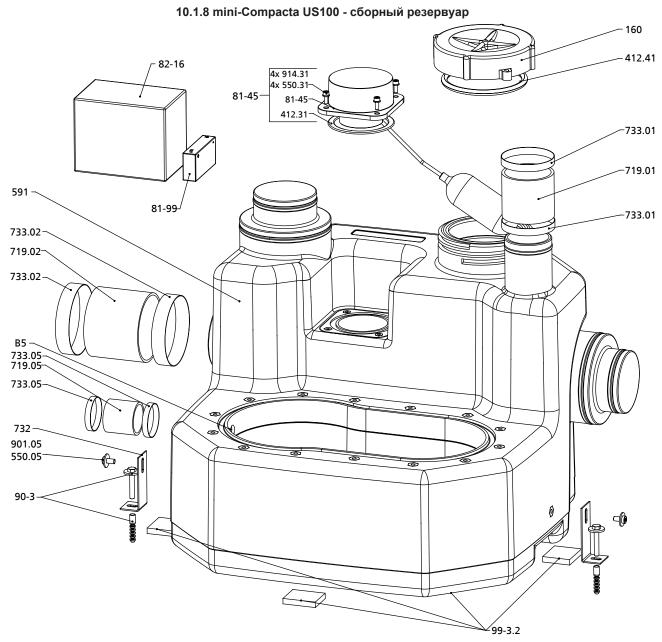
Покомпонентный сборочный чертеж mini-Compacta US100 — сборный резервуар
